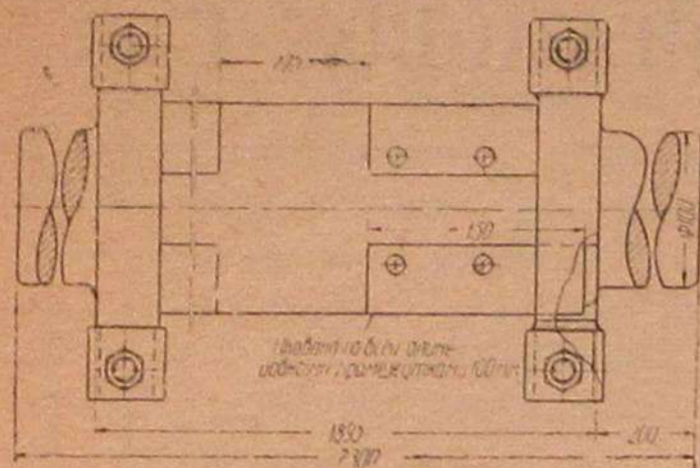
Приспособление для изготовления корпуса-очистителя-охладителя.
